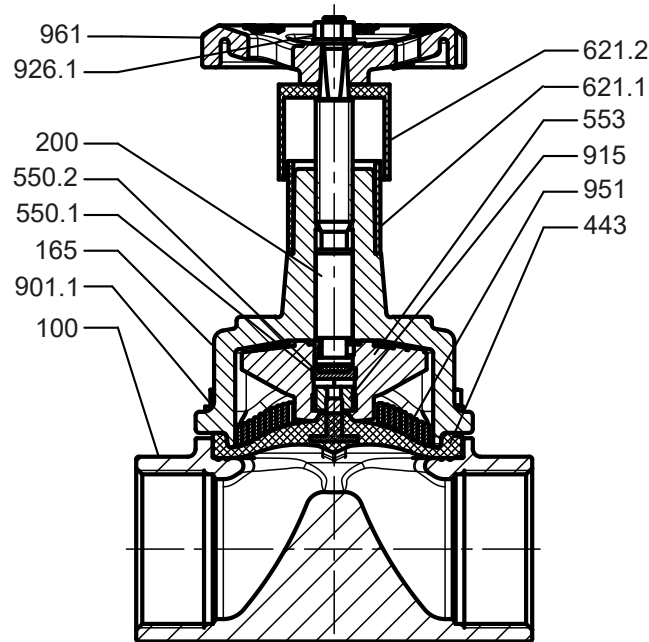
Handventil SISTO-16 mit Flanschanschluss
